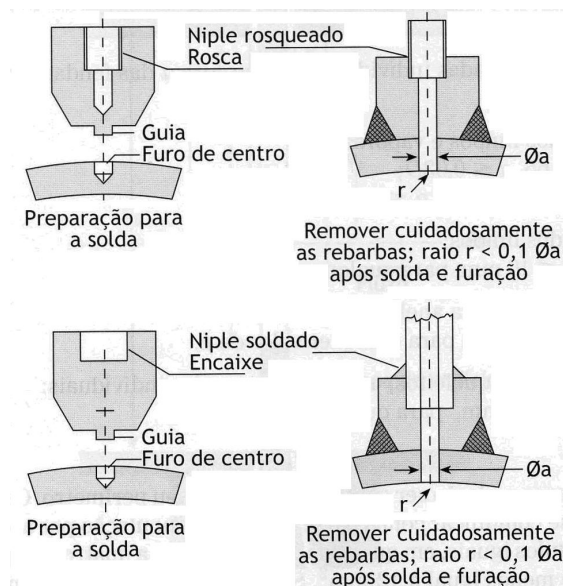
Tomadas Δp soldadas na tubulação
